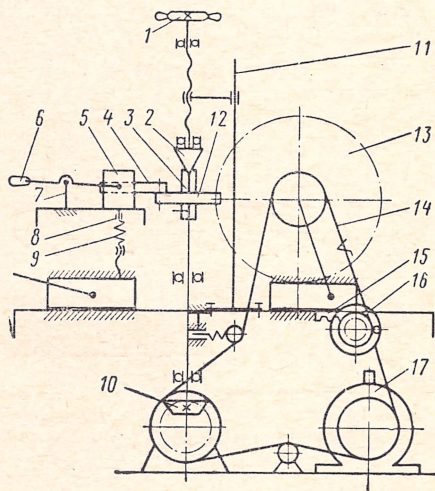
Станок для безопасной зачистки заусенцев на шестернях
